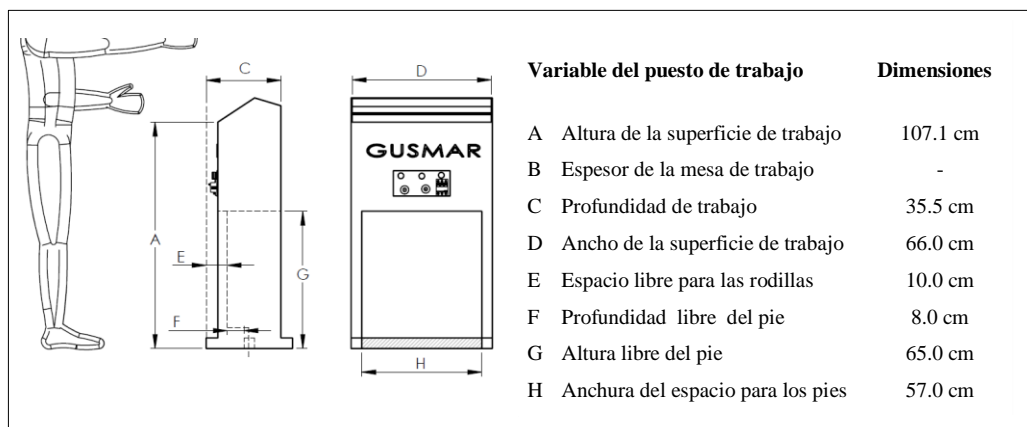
Dimensiones actuales del puesto de vaporizado de cortes
